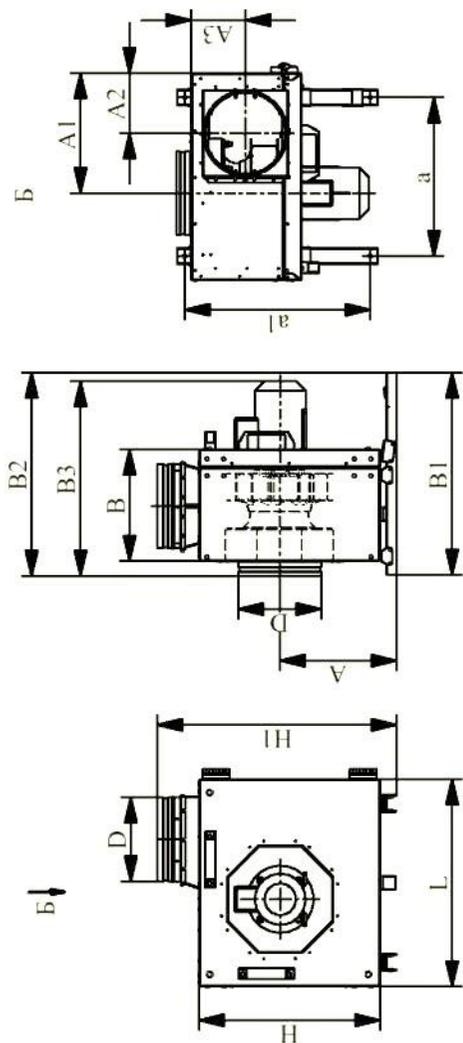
Габаритные и присоединительные размеры вентилятора
